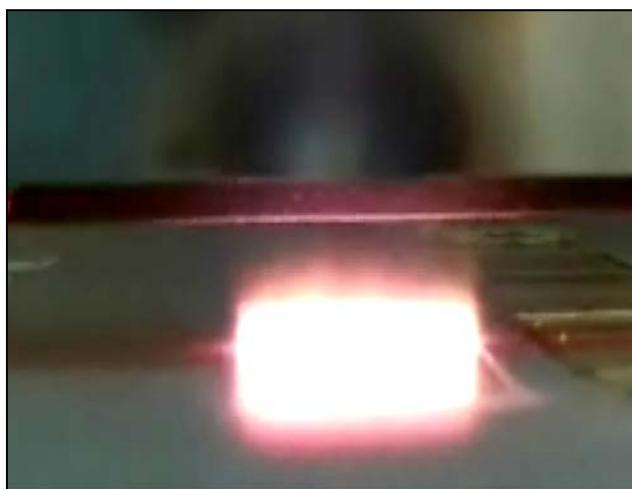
Приповерхностная лазерная плазма, образующаяся при лазерно-плазменной очистке поверхности
